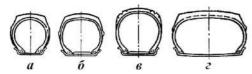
Поперечные сечения (профили) шин различного типа: a – обычной конструкции; δ , ϵ – с регулируемым давлением воздуха; ϵ – широкопрофильных
